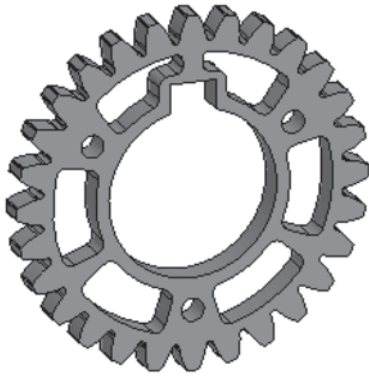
3D-модель листовой выкройки цилиндрической прямозубой шестерни
